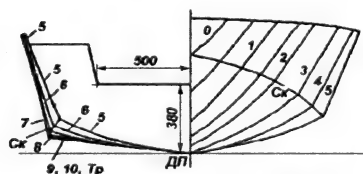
Теоретический корпус мотолодки «Крым-3»
